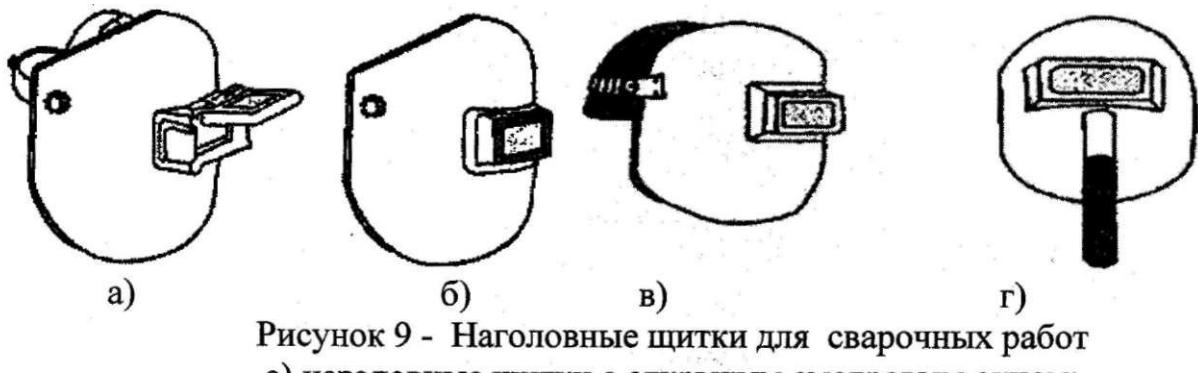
Наголовные щитки для сварочных работ
